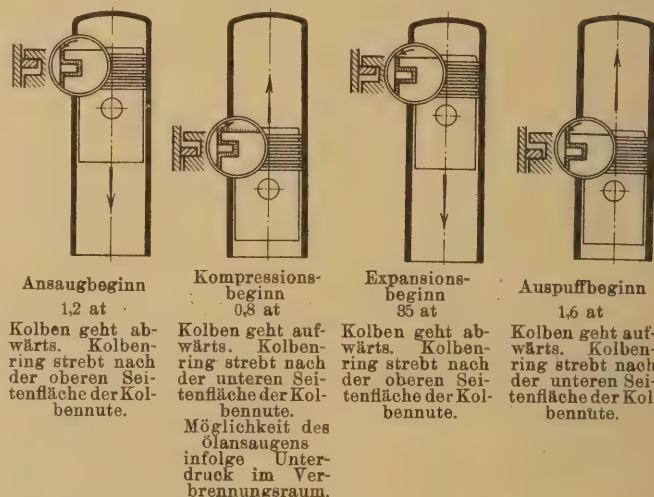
bis 14. Schmierung einer ortfesten Dieselmachine.
